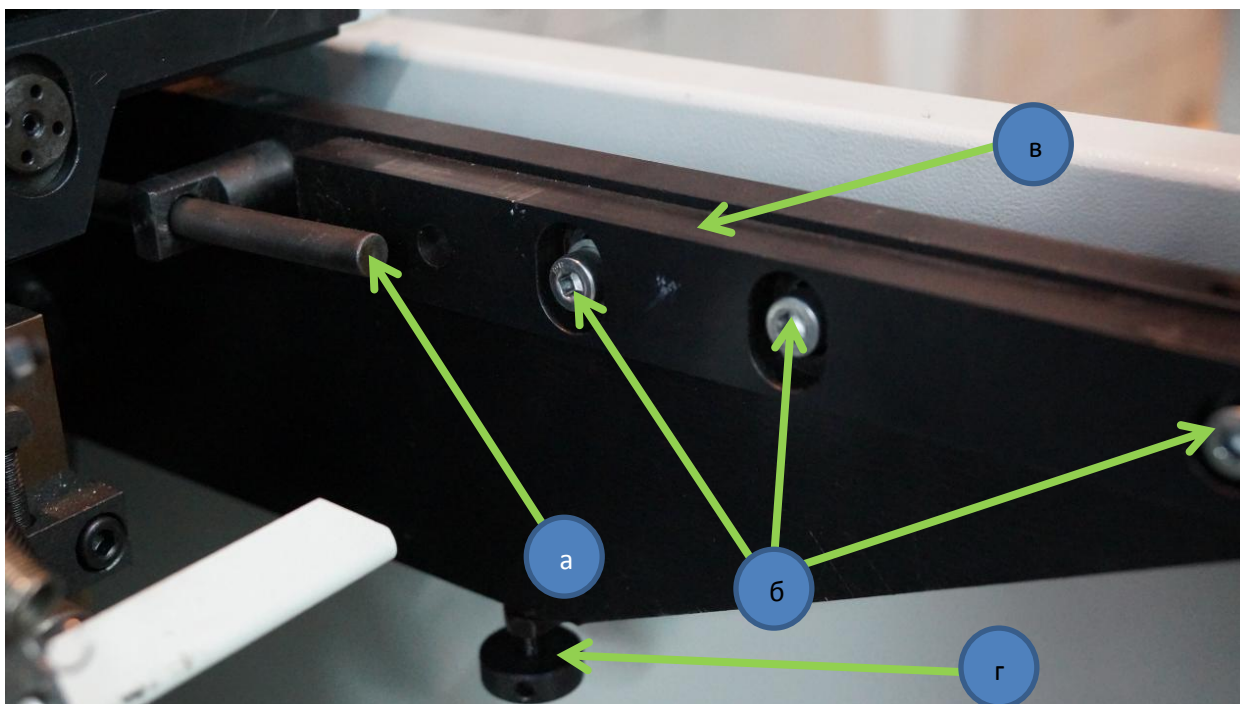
Подвижный толкатель стола: а-подвижный толкатель; б- болты крепления направляющей стола; в- направляющая стола; г – регулировочный винт положения направляющей стола с контргайкой
